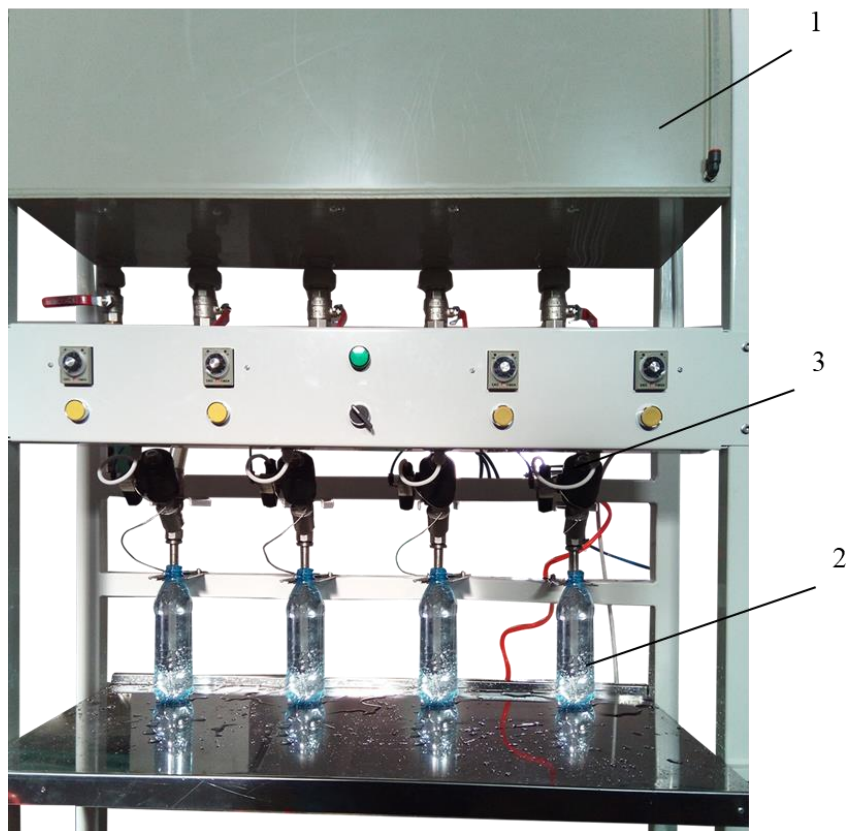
Загальний вид компоновки досліджуваного потокового дозатора: 1 – бункер живильник; 2 – споживча упаковка (ПЕТ пляшка); 3 – сідельний керований клапан.
